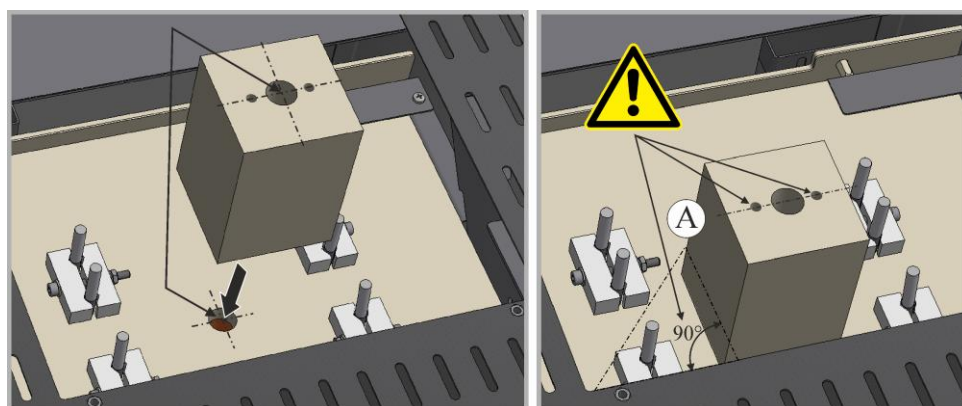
Montering av isoleringsblocket (liknar det på bilden)
